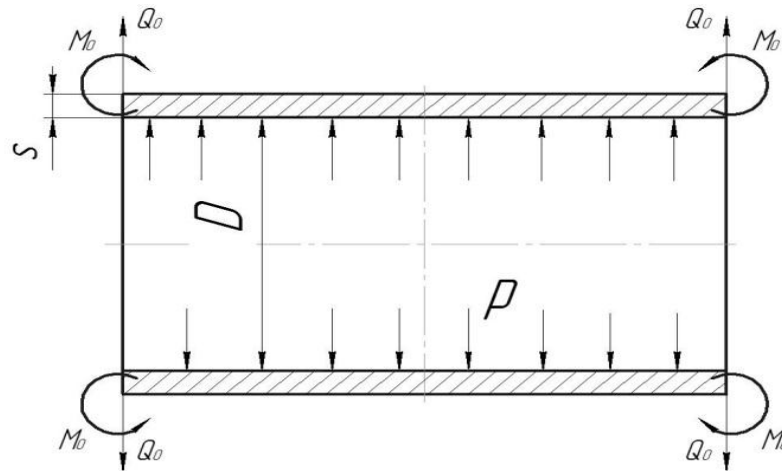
Розрахункова схема циліндричної обичайки
